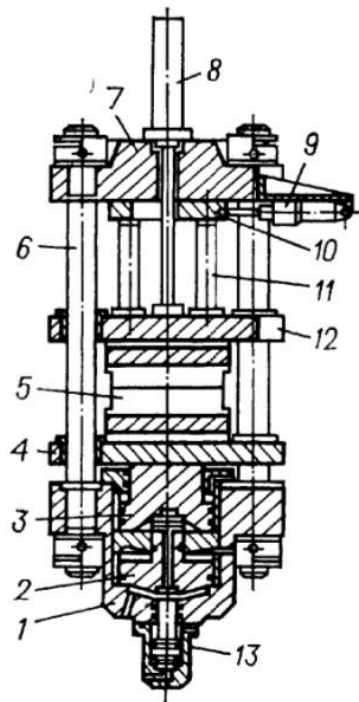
Формодержатель багатопозиційної литвевої машини:
